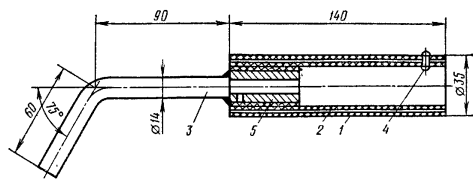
Электрододержатель для безогарковой сварки:
